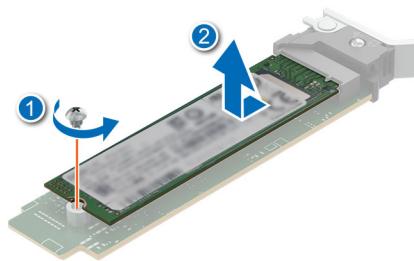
Entfernen des M.2-SSD-Laufwerks
